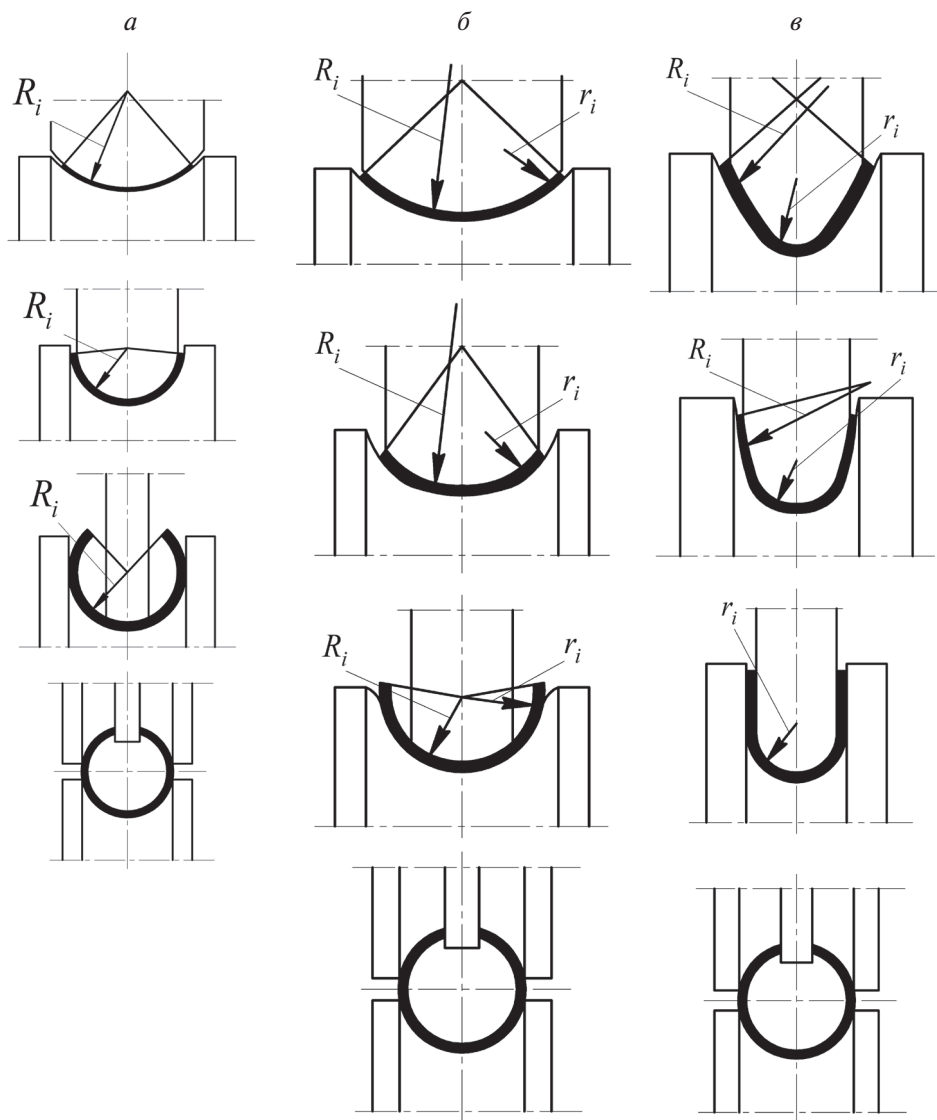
Схемы формовки трубной заготовки на валковых формовочных станах:
